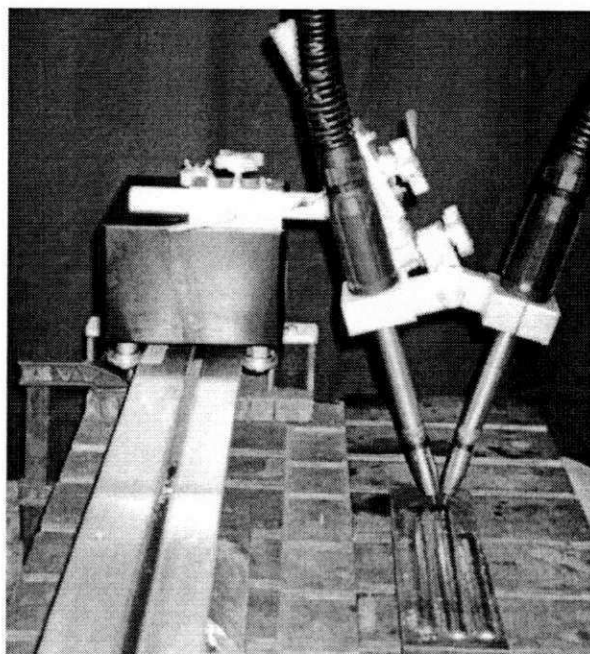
Soldagem executada com o processo MIG/MAG com duplo arame com eletrodos posicionados lado a lado. Fonte: Motta (2000)
